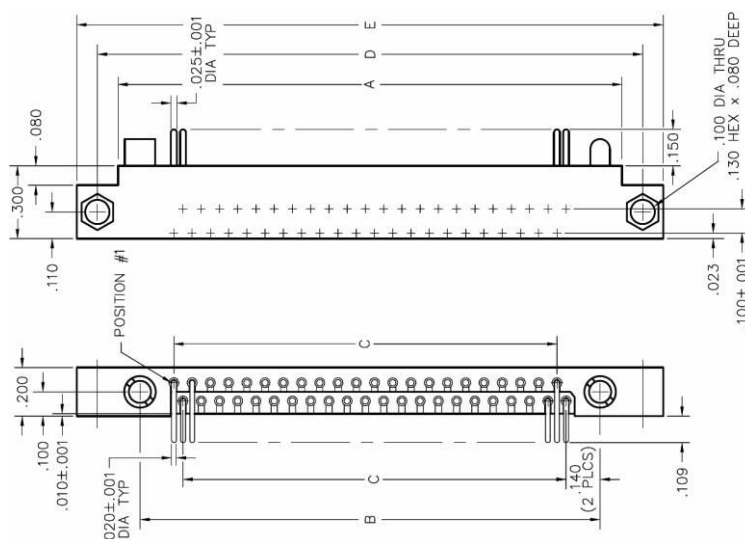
AirBorn/JONHON CRM252-040-xx1-xxxx 插头尺寸 (1.905 mm 间距).
